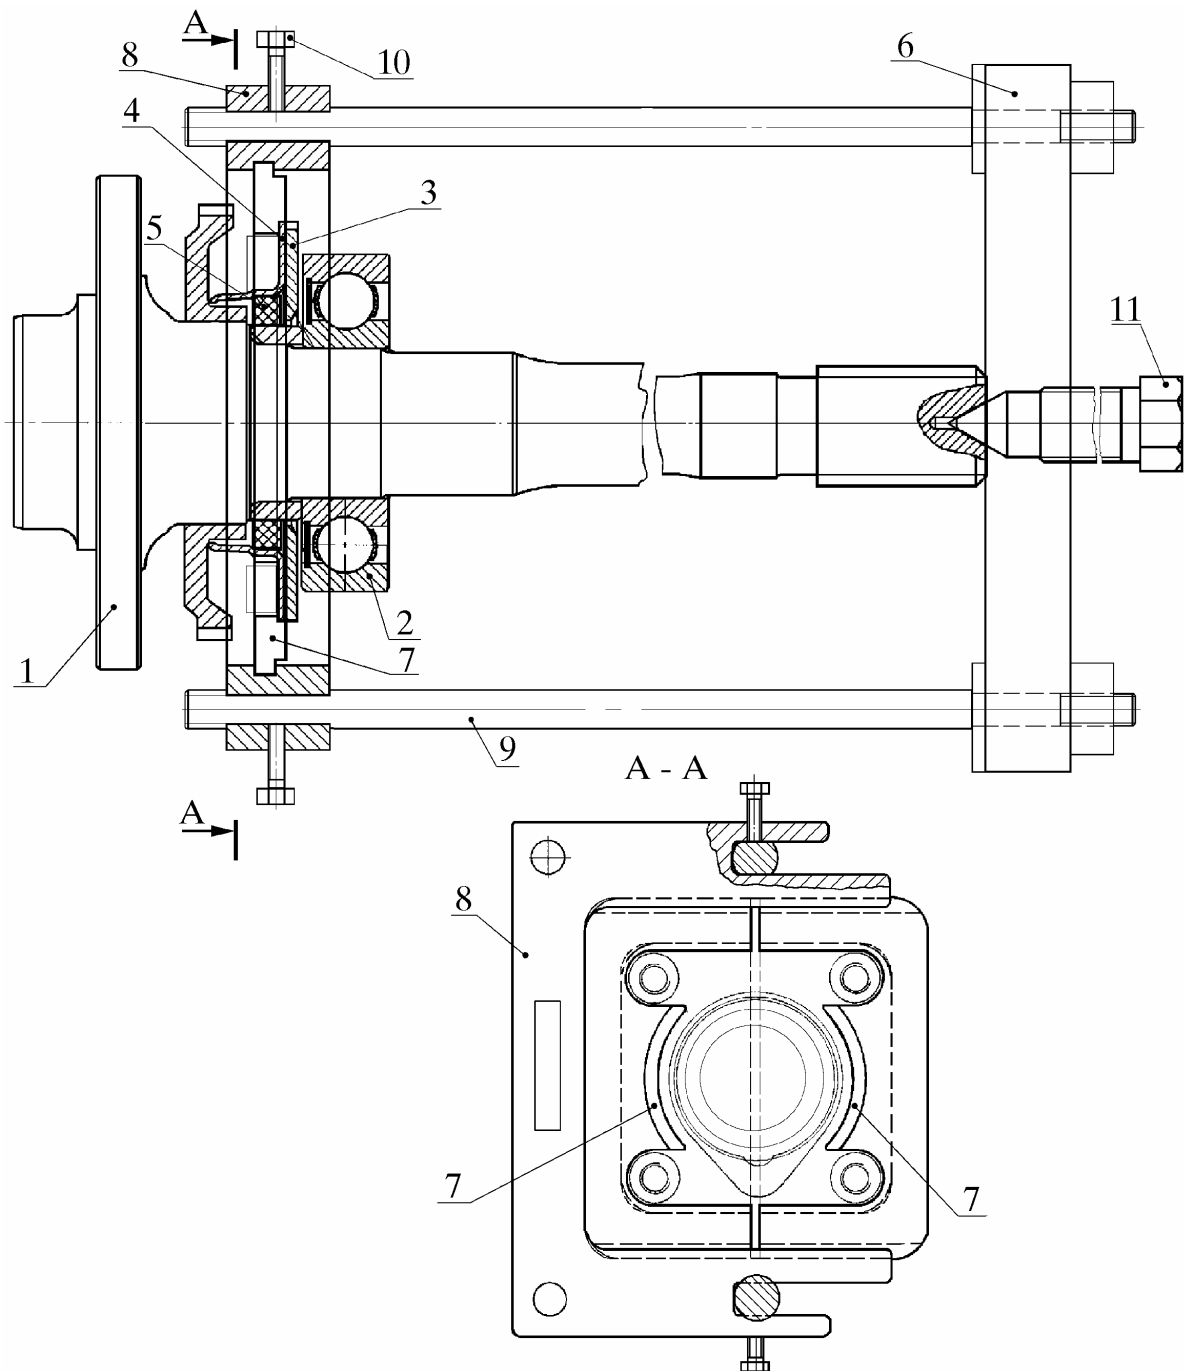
Снятие подшипника, пластины, корпуса наружного сальника и сальника: 1 - полуось заднего моста в сборе; 2 - подшипник; 3 - пластина; 4 - корпус наружного сальника; 5 - сальник; 6 - съемник 6991-4636; 7 - вкладыш 6991-4636.00.02; 8 - каретка; 9 - шпилька; 10, 11 - болты
